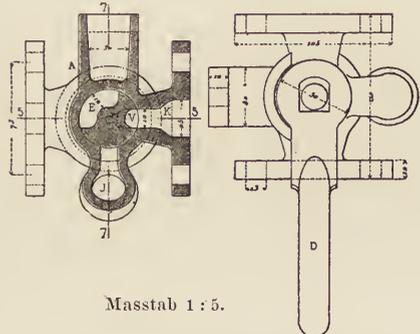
Querschnitt nach 6,6. Fig. 12. Grundriss.
